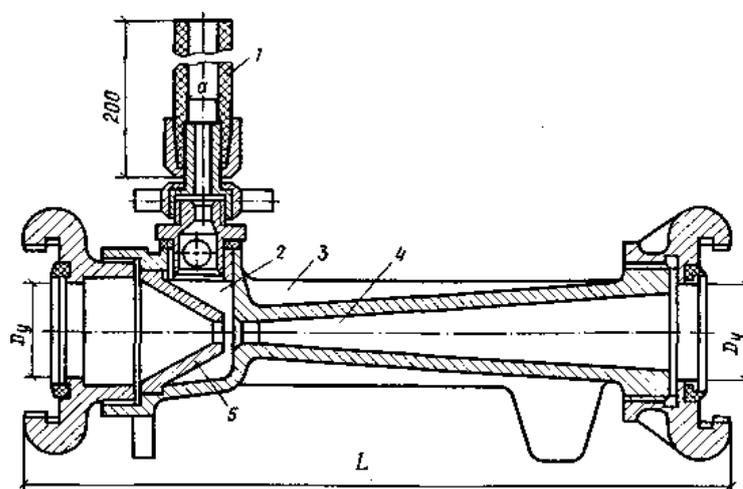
Пеносмеситель ПС-1: 1 – всасывающий шланг; 2 – рабочая камера; 3 – корпус; 4 – диффузор; 5 – сопло
